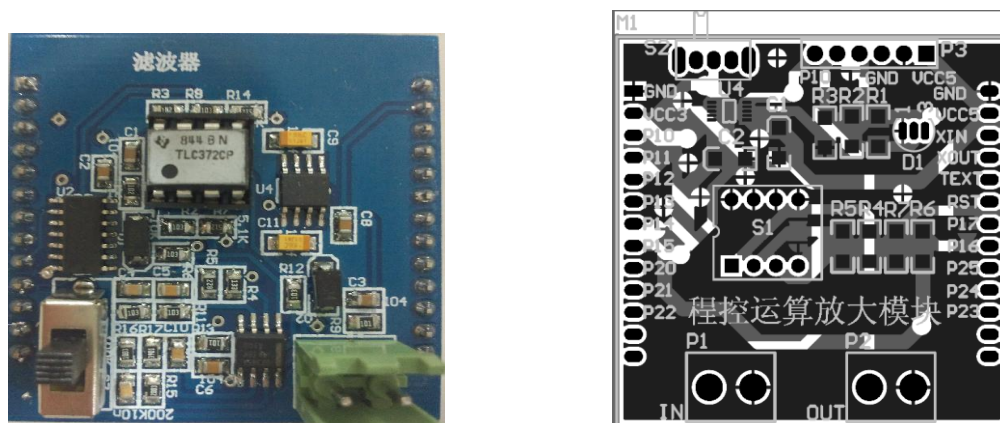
模拟滤波器模块实物图及 PCB 图
